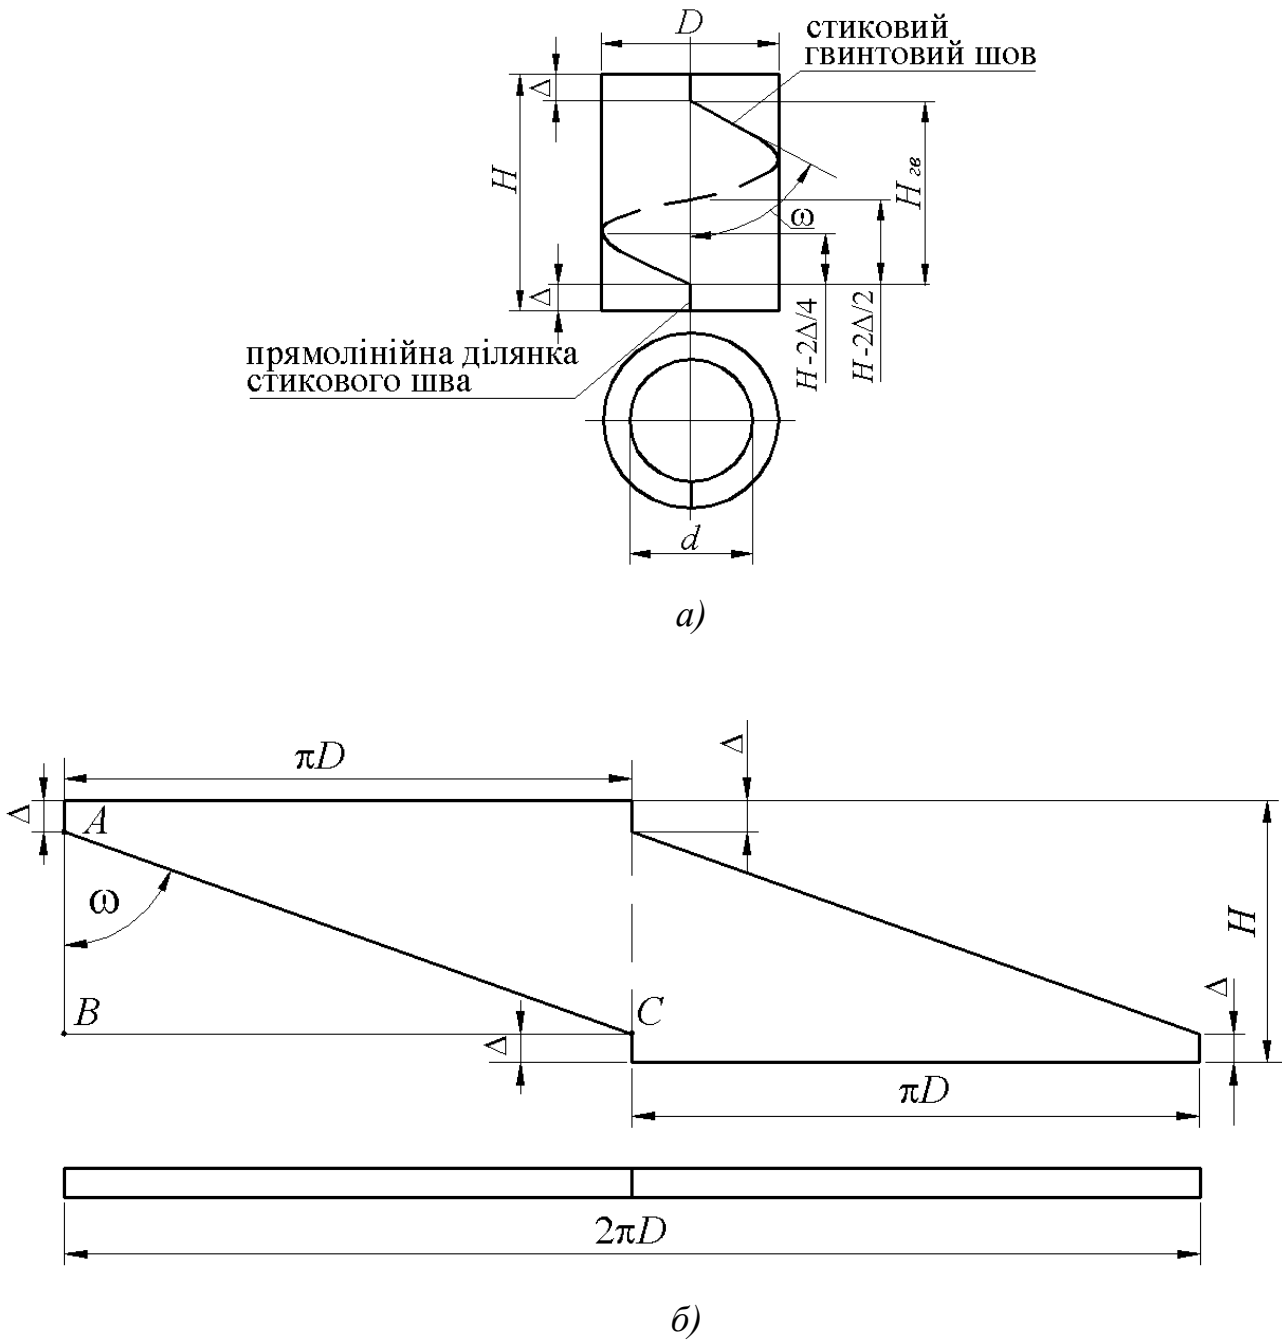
Схематичне зображення згортої втулки нової конструкції – а) і її розгортки – б)
